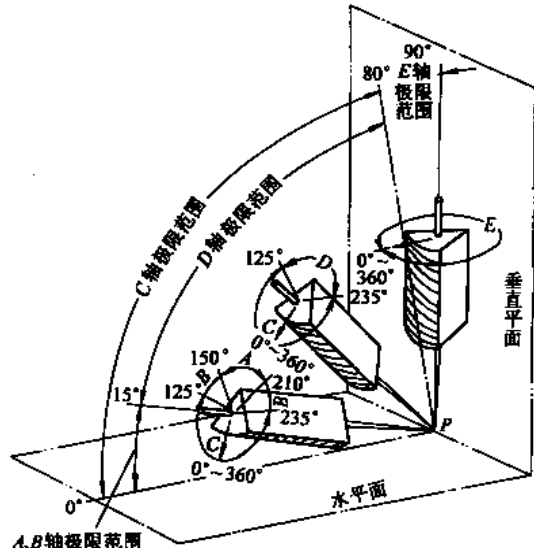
角接焊缝试板和管材试件的焊接位置
